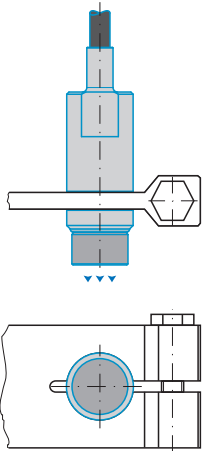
Geschirmter Sensor mit Gewinde in Standardmontage
